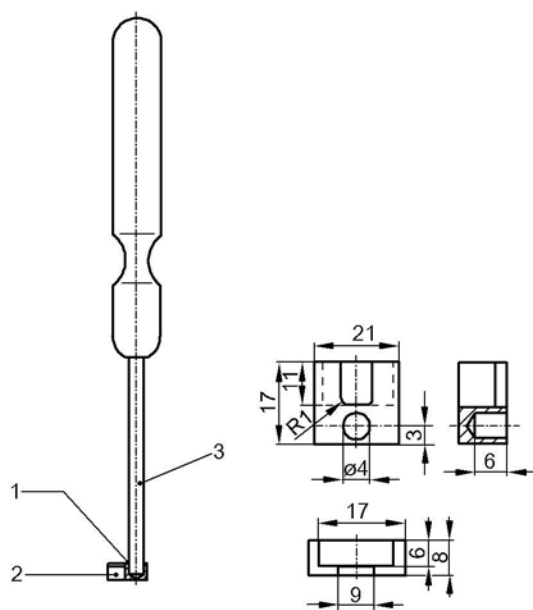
Attrezzo per inserire il capocorda a spina sulle bobine a solenoide
